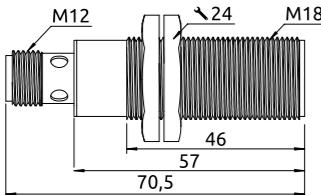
Габаритные размеры UDS.18-100-, мм
